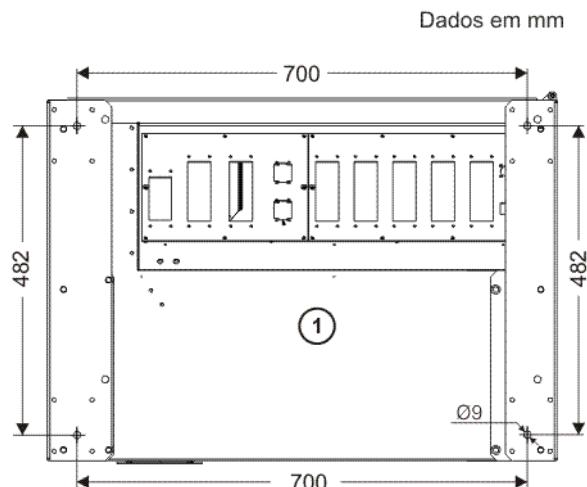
Dimensões e medidas de furos do suporte do smartPAD
